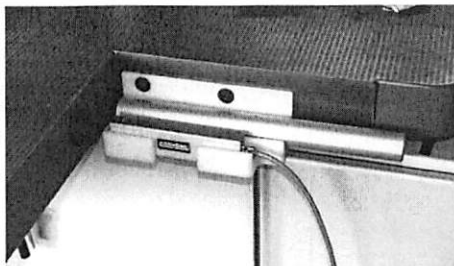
Halter für HSK-Schlüssel u. Zeromaster
